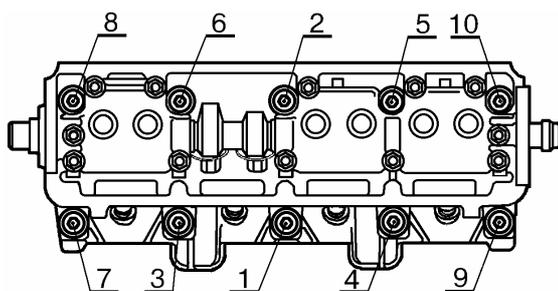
Порядок затяжки болтов крепления головки цилиндров.
